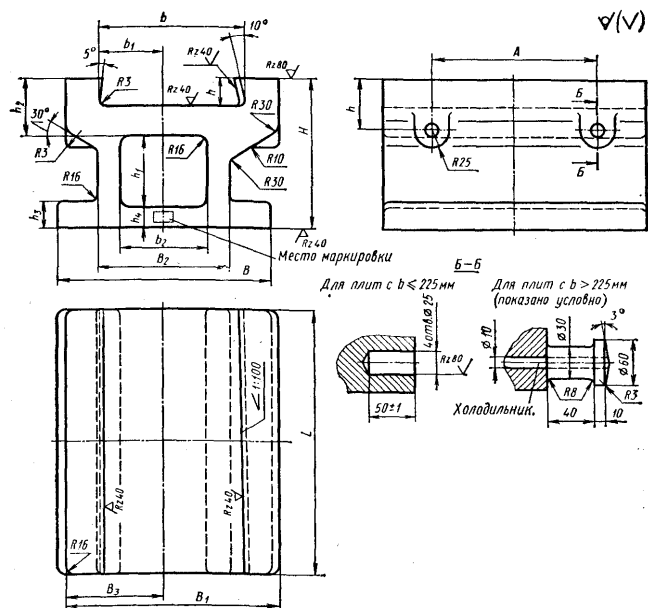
Размеры нижней коробчатой плиты для крепления матриц клином
